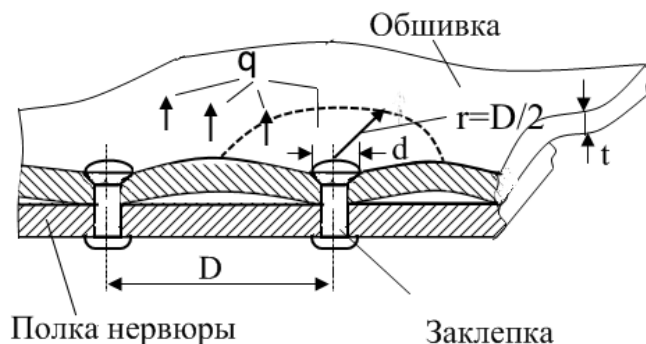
Схема заклепочного ряда крепления обшивки к полке нервюры.
